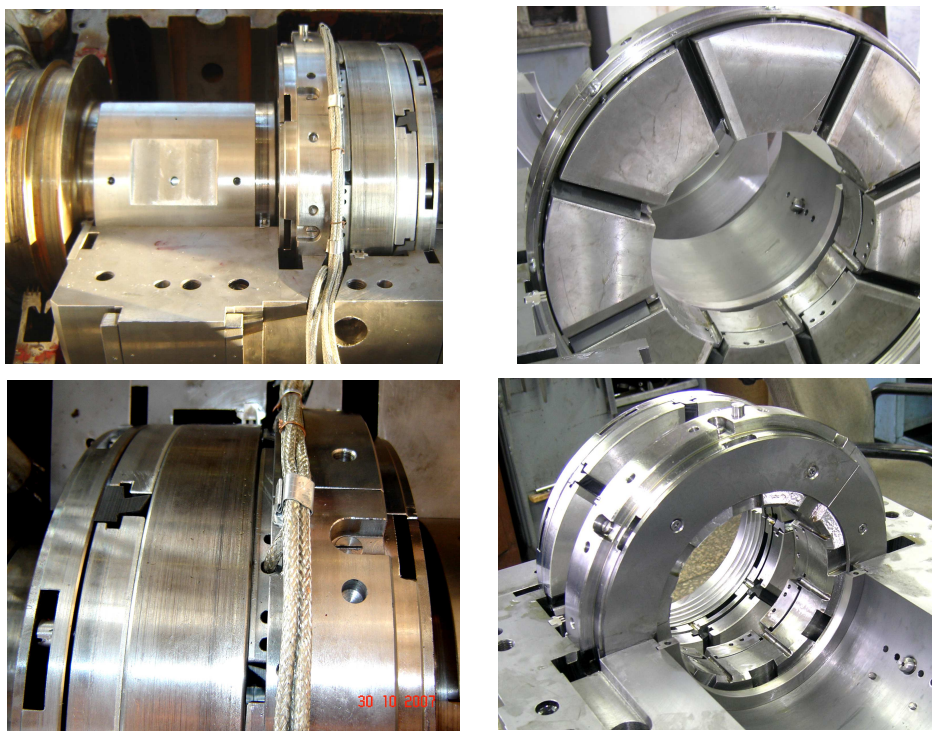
Демпферный опорно-упорный подшипник паровой турбины К15-41
